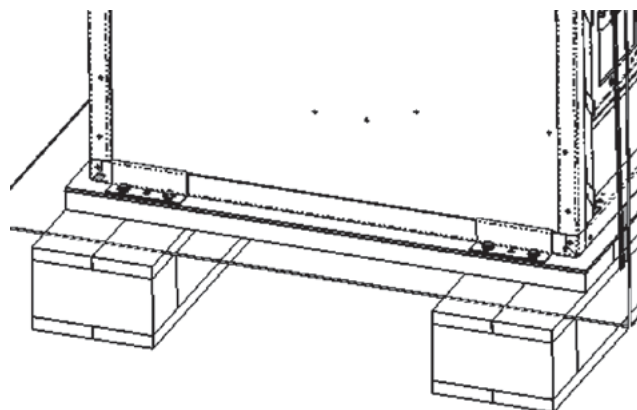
Placas de montaje en el exterior de la unidad 750 mm
